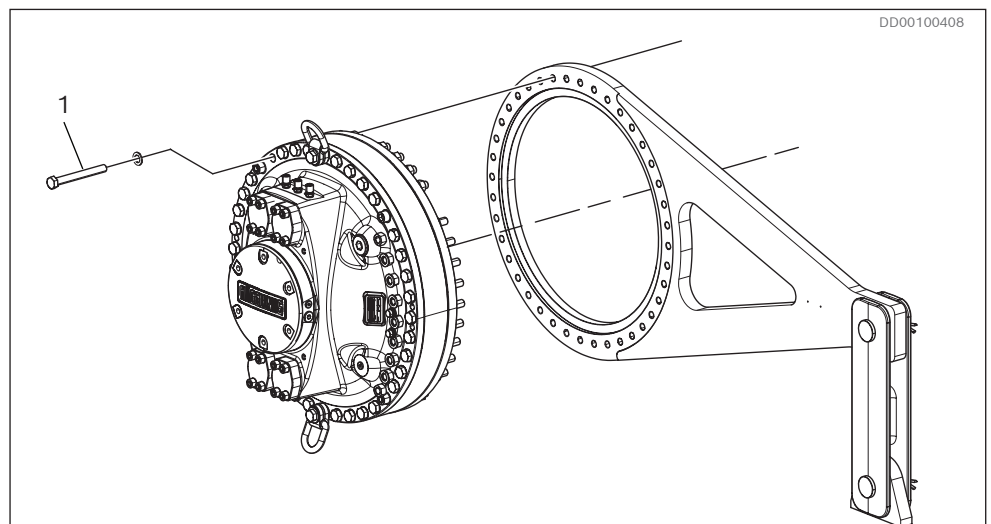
Montage von einseitiger Drehmomentstütze TC A 0400 für CB 280 bis CB 400
